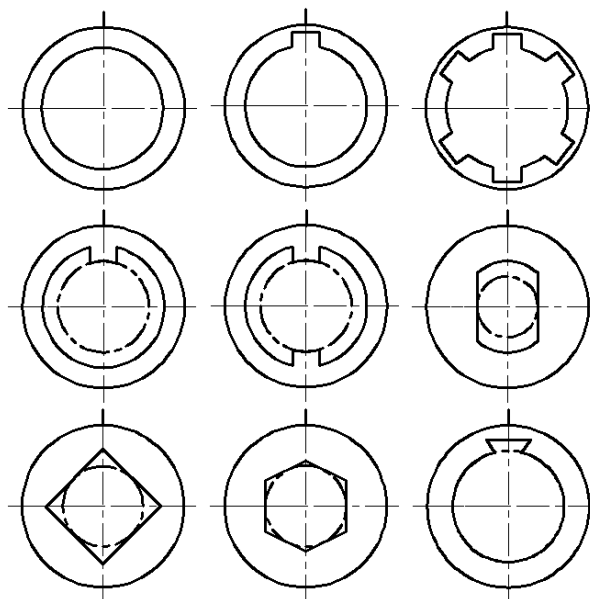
Профили деталей, обрабатываемых внутренним протягиванием
